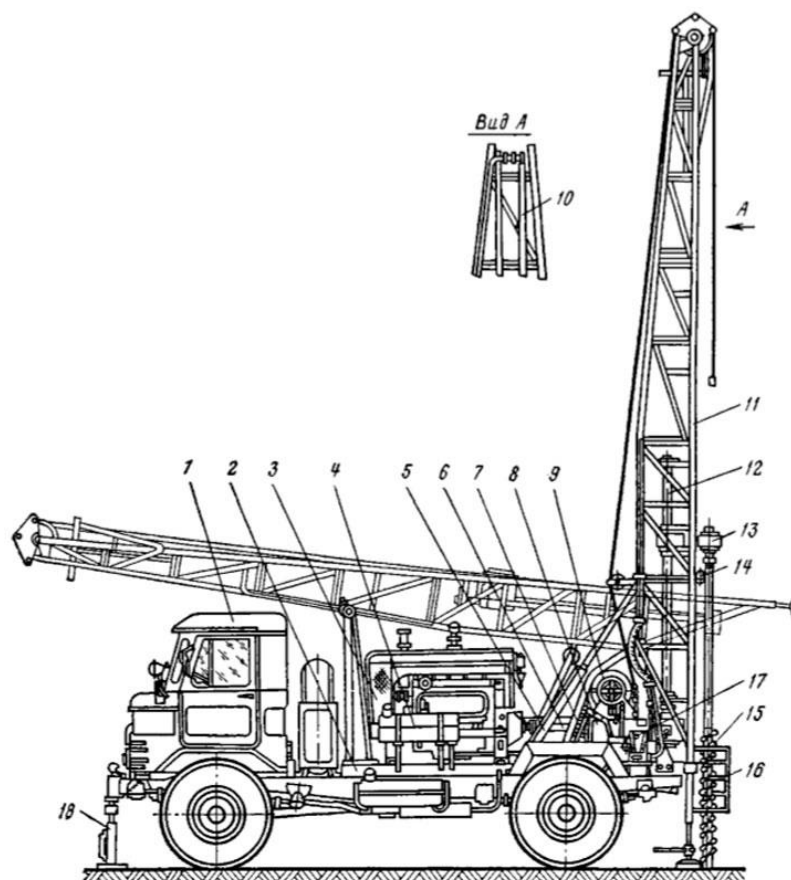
Буровая установка на шасси ГАЗ-66:
